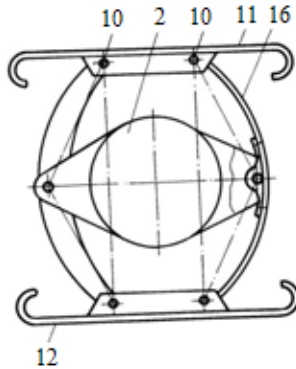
Варіант рушія з двома опорними башмаками:
